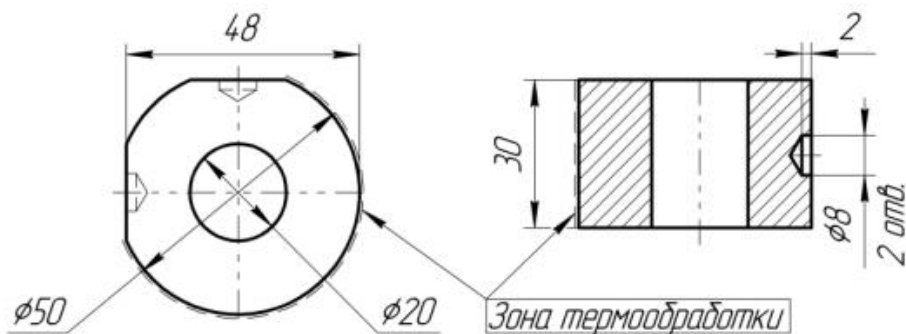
Геометрические размеры образца для плазменной закалки.
